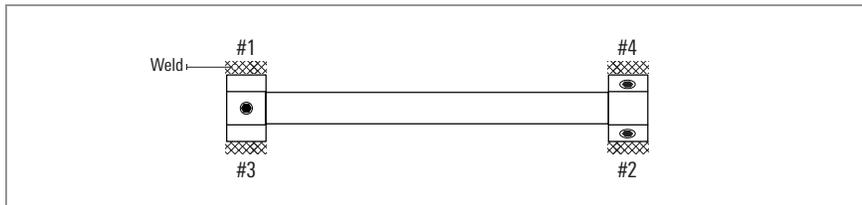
Secuencia de soldado para los bloques de montaje
